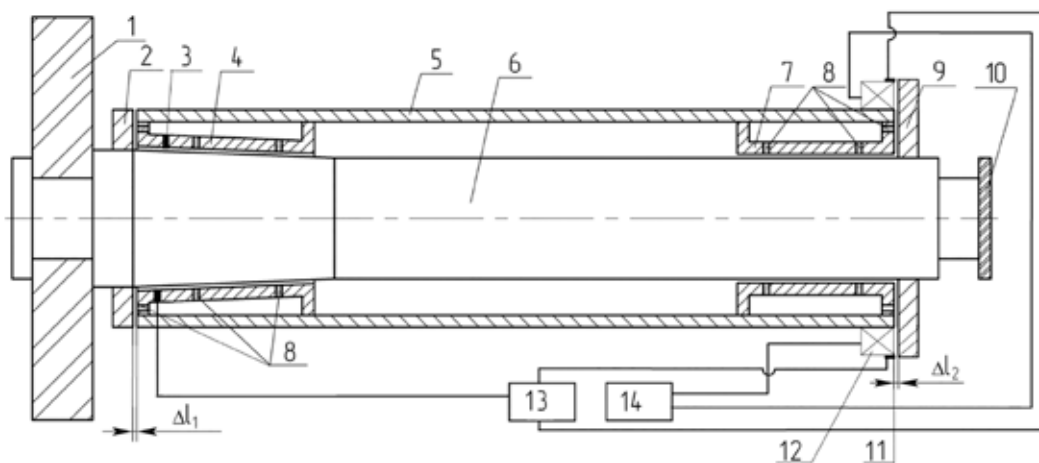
Управление шпиндельным узлом на газостатических опорах с передней опорой малой конусности: 1 – шлифовальный круг, 2, 9 – подпятники, 3, 11 – датчик зазора, 4 – передний газостатический подшипник с малым углом конусности, 5 – корпус шпиндельного узла, 6 – шпиндель, 7 – задний цилиндрический газостатический подшипник, 8 – пористые вставки, 10 – приводное колесо, 12 – электромагнит 13 – АЦП, 14 – блок управления
